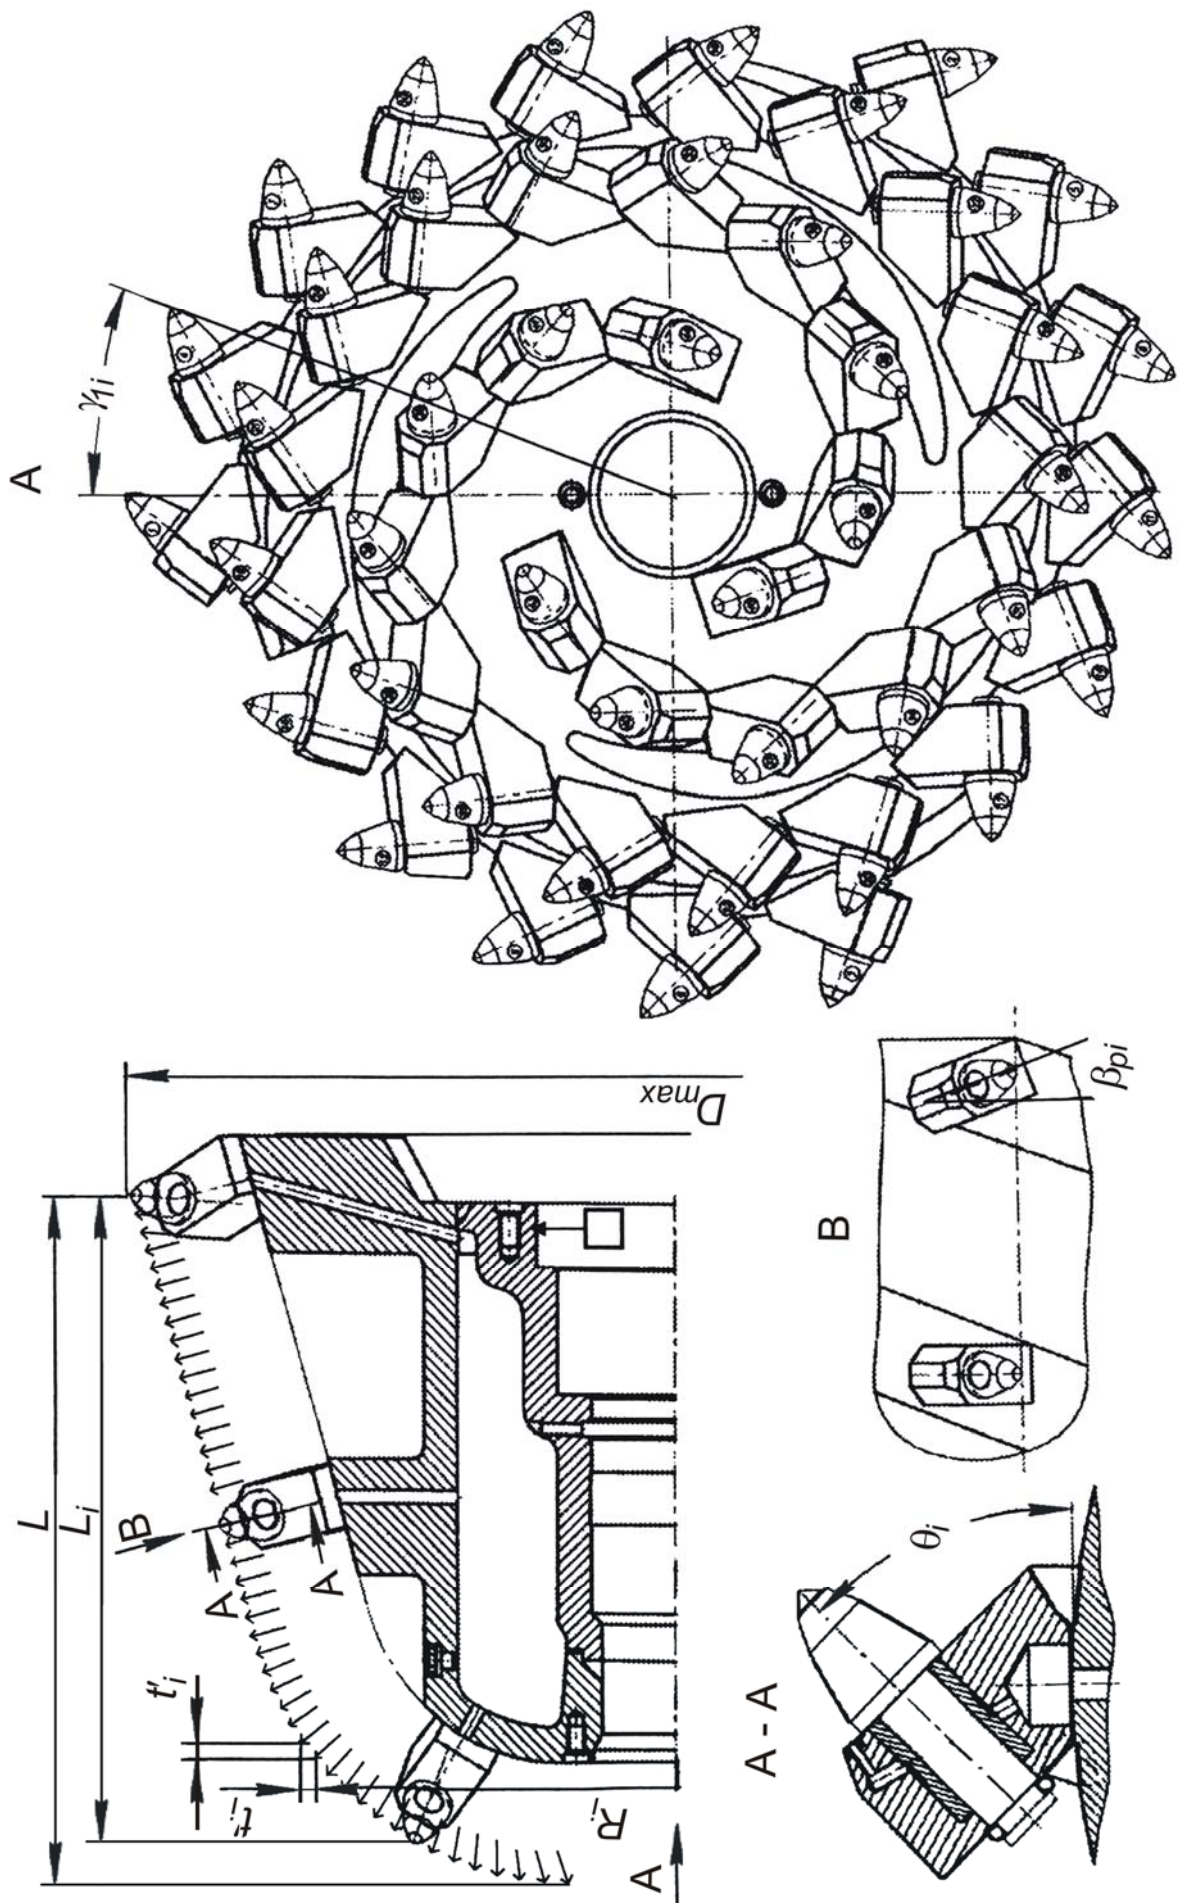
Поздовжно-осьовий фрезерний виконавчий орган
